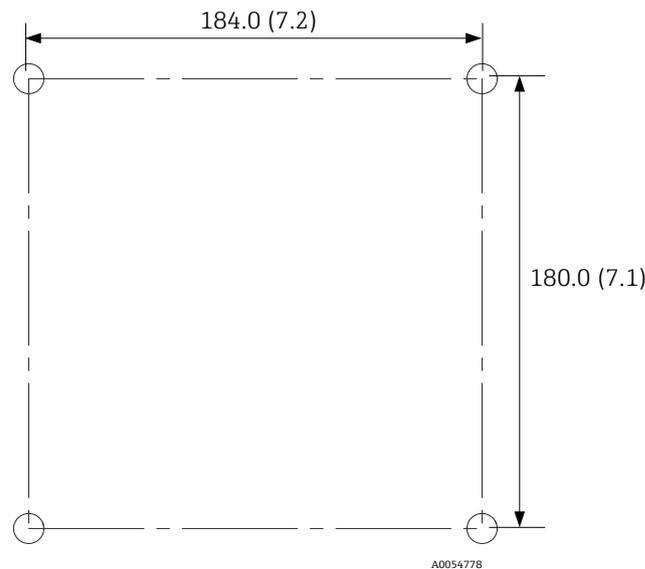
Schéma des trous de montage du boîtier MAC. Dimensions : mm (in)
